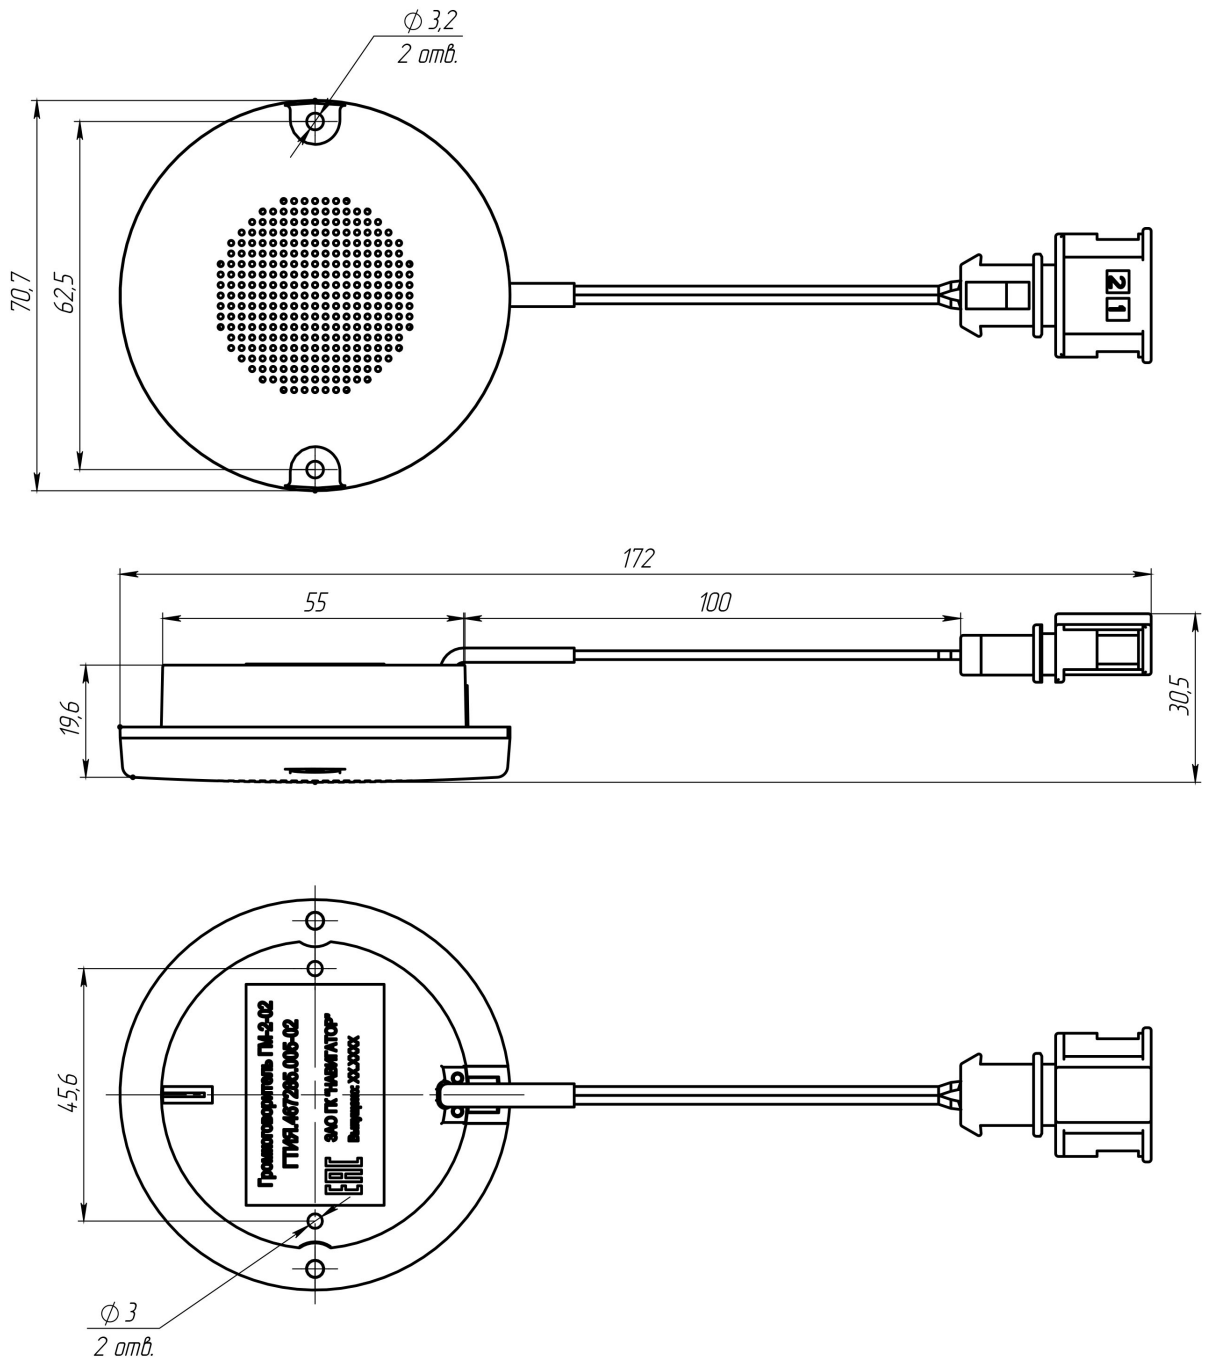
Габаритный чертёж Громкоговорителя ГМ-2-02
